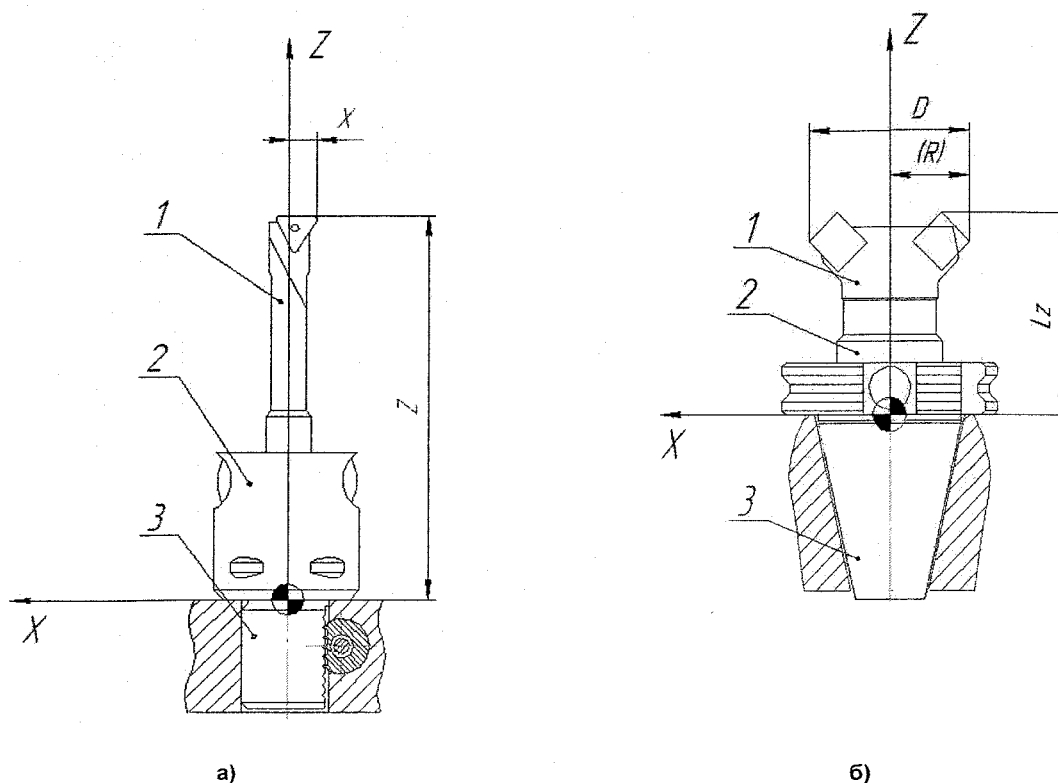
Схема определения размеров настройки инструментальных комплектов: 1 – РИ; 2 – оправка; 3 – хвостовик.; а – прибор НИИК-2026 для токарных станков; б – прибор НИИК-2027 для станков СФР группы
